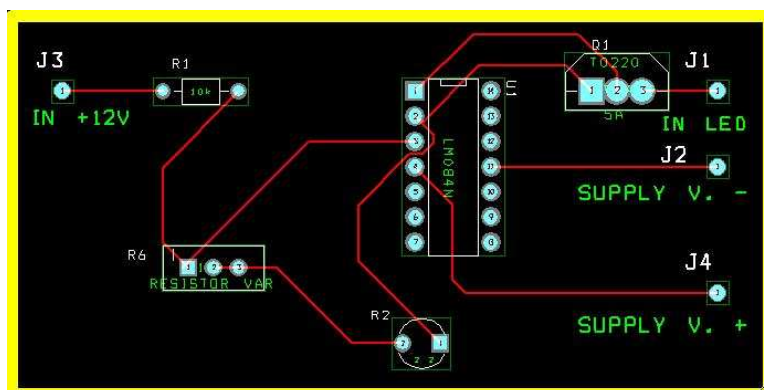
Captura del diseño de la placa de control con Orcad Layout
